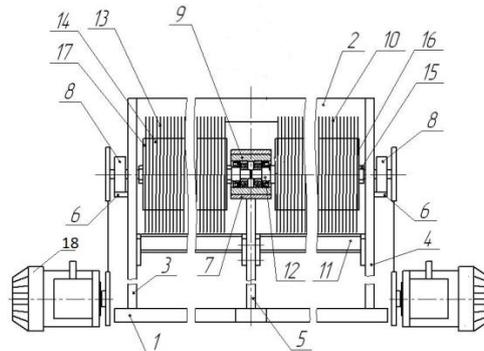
Принципиальная схема усовершенствованной конструкции волоконоочистителя: 1 – рама; 2 – корпус волоконоочистителя; 3-4 – крайние стенки; 5 – средняя стенка перегородка; 6 и 7 – опоры; 8 и 9 корпуса подшипников; 10 – пыльный цилиндр; 11 – колосники; 12 – пыльные валы; 13 – пилы; 14 – междупильная прокладка; 15 – затяжные гайки; 16 – косая шайба; 17 – шпонка; 18 – электродвигатель
